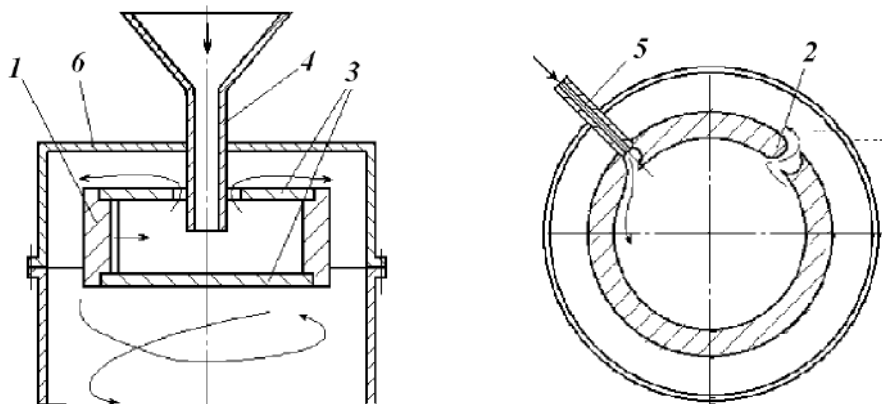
Вихревая мельница: 1 – помольная камера; 2 – узел вывода газозвеси; 3 – верхняя и нижняя торцевые крышки; 4 – питающая воронка; 5 – патрубок подачи сжатого воздуха; 6 – пыленепроницаемый кожух.
